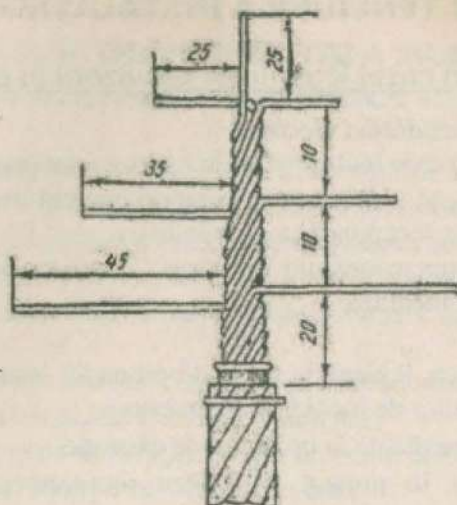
Conductor multifilar din aluminiu, cu secțiunea de  $120 \text{ mm}^2$  desfăcut pentru metalizare
